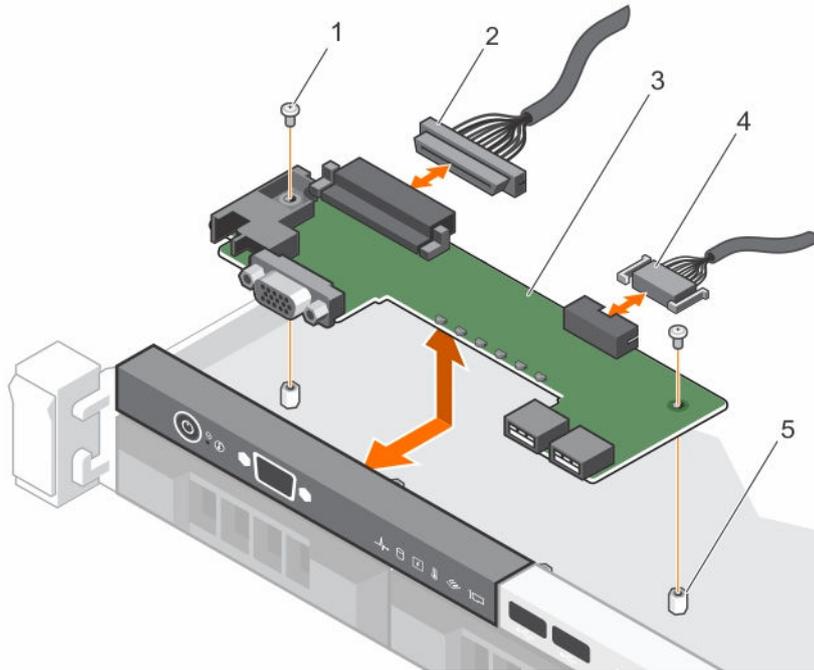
Remover e instalar a placa do painel de controle de LED — chassi de quatro discos rígidos com cabo
